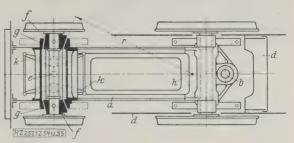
und 55. Laufrad-Triebrad-Drehgestell mit Adamlaufachse und im Hauptrahmen gelagertem Motor. (Schweiz, Lokomotiv- und Maschinenfabrik - M. Weiß)
